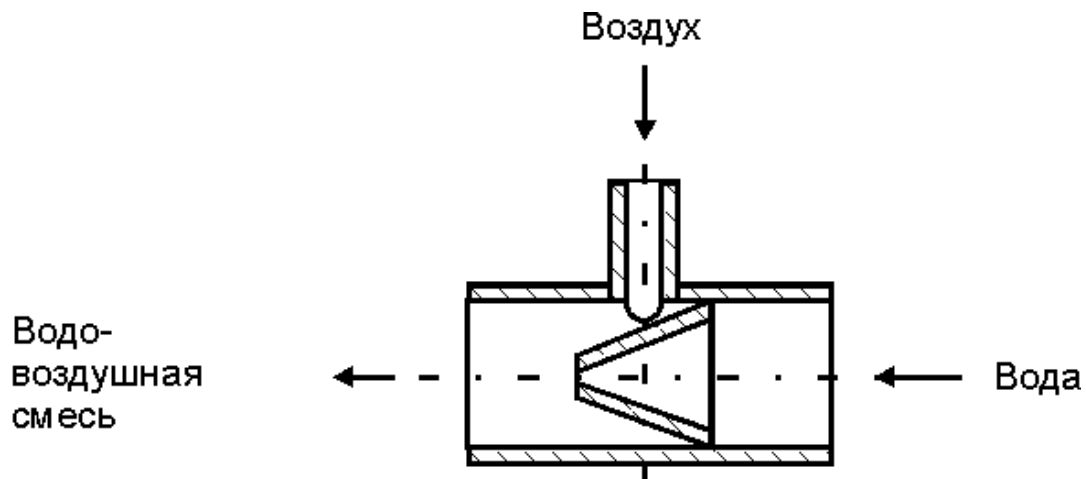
Эжектор: 1 - патрубок для воды; 2 - сопло; 3 - патрубок для воздуха; 4 - камера смешения.
